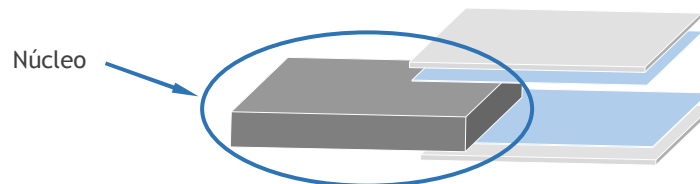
Núcleo em espuma metálica da estrutura sandwich.
